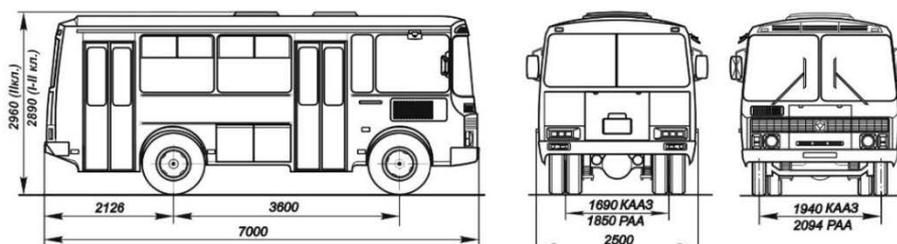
Габаритные размеры автобуса ПАЗ-32054
